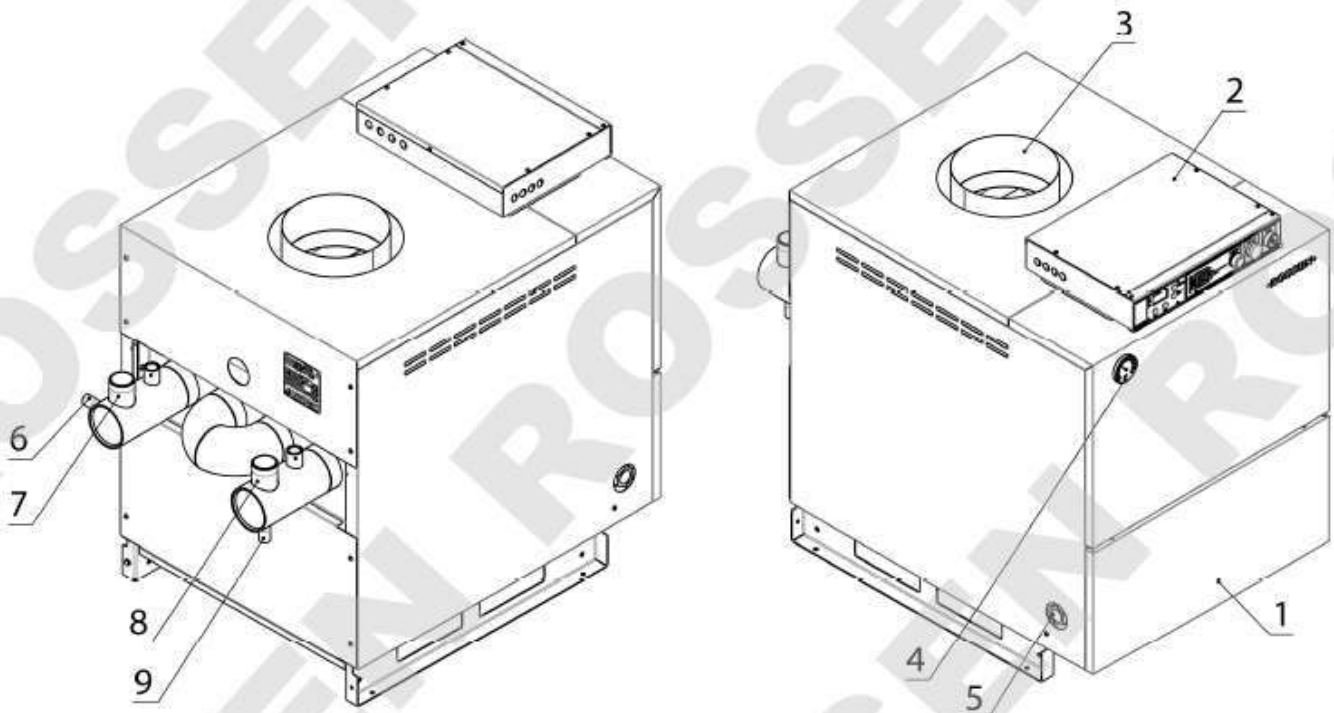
Габаритно-присоединительные размеры котла RSA60
